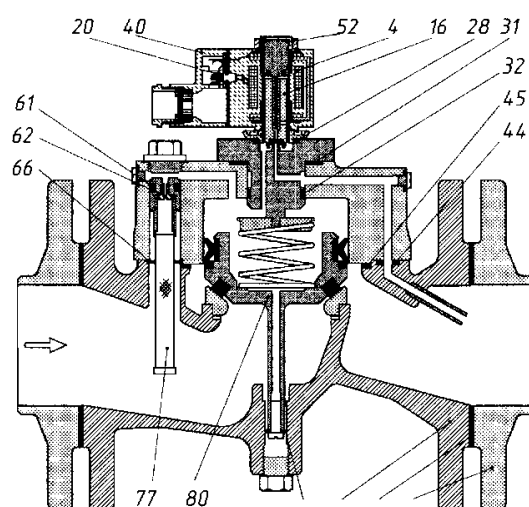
Устройство соленоидного клапана *EVSI65*: 4 — обмотки; 16 — сердечник; 20 — заземление; 28 — уплотнение; 31, 32 — кольцевое уплотнение; 45 — уплотнение крышки клапана; 47 — фланцы; 49 — корпус клапана; 50 — уплотнение; 52 — крышка; 61, 66 — кольцевое уплотнение; 62 — дюза; 77 — фильтр; 80 — сервопривод
